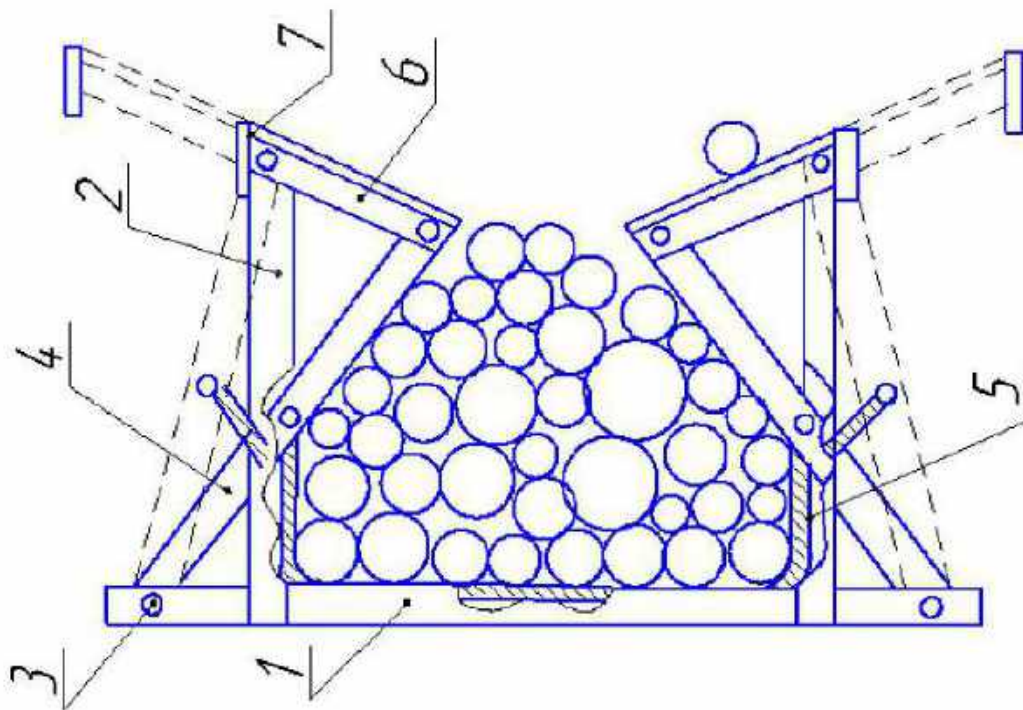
Важільний пакетоформувальний пристрій
